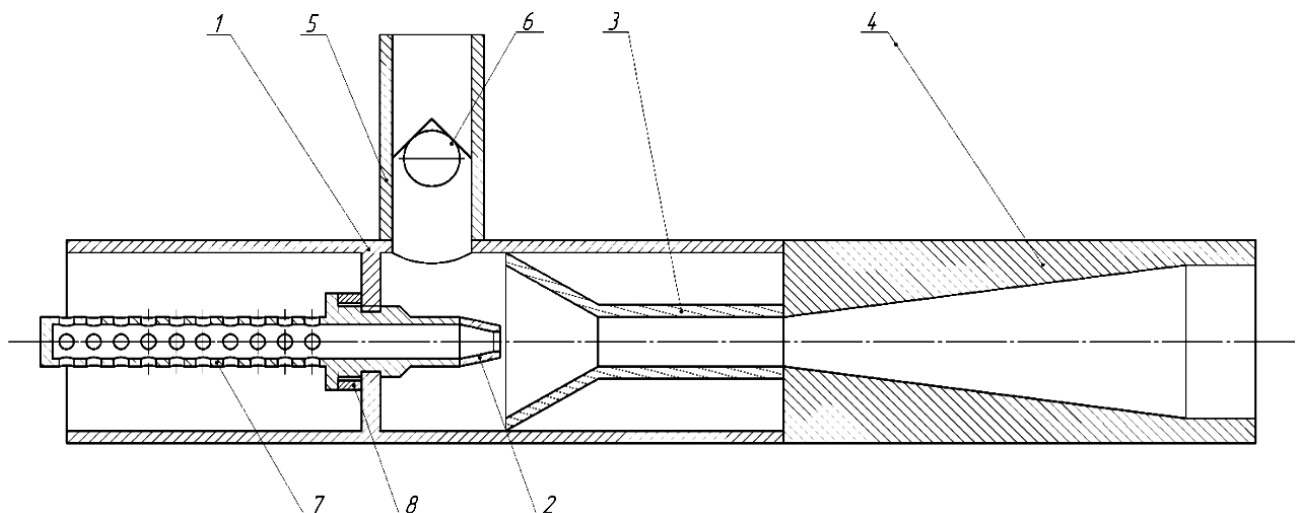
Схематичний вигляд пристрою для освоювання свердловин піною в розрізі
